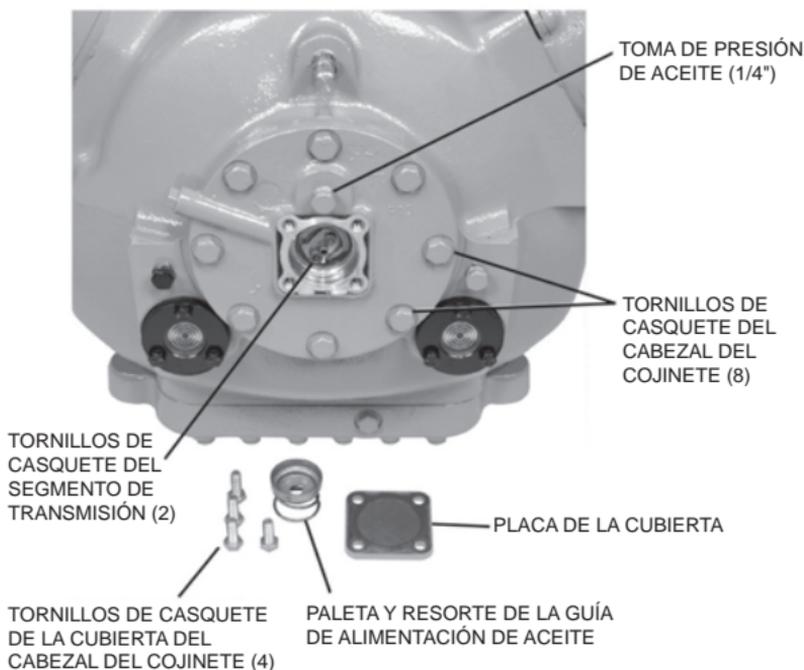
Extracción del cabezal del cojinete del extremo de la bomba (compresor 06E)
